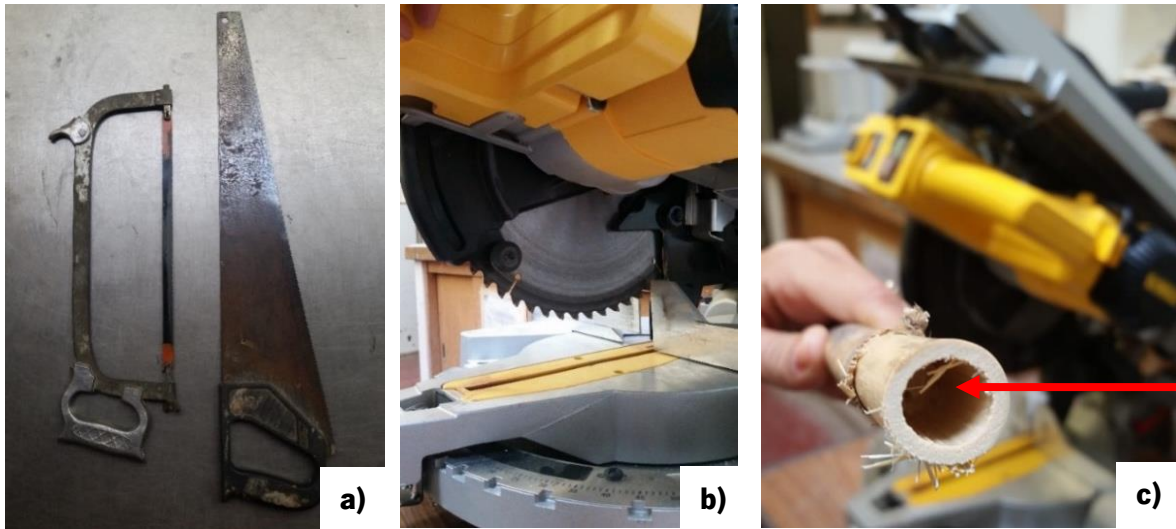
Ferramentas de cortes testadas: serrote de fita e serrote reto (a); máquina elétrica de corte (b); resultado de corte com máquina elétrica (c).
